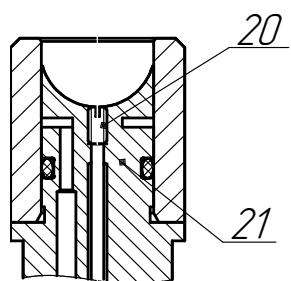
Положение капилляра в корпусе сопла калибратора
